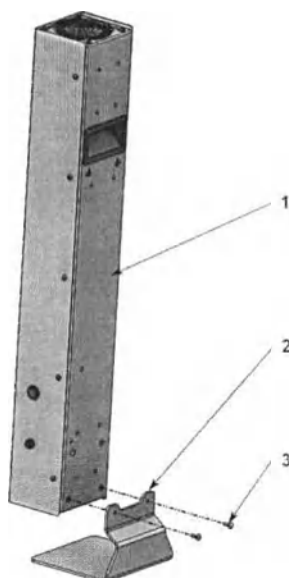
Монтаж облучателя РП-30 и РП-40 на опорную стойку. 1- Облучатель; 2- Опорная стойка; 3- Винт М5
